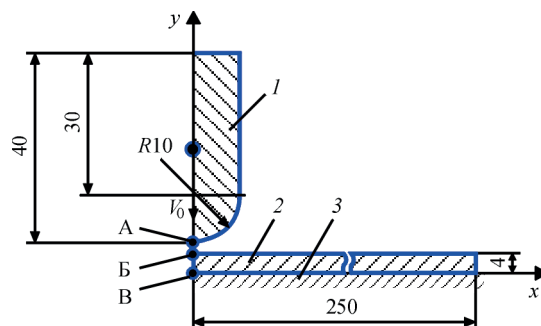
Розрахункова схема процесу динамічного навантаження пластин, що обробляються ЕДО: 1 – електрод-індентор; 2 – зразок, що обробляється; 3 – абсолютно жорстка основа, 4 – точка на зовнішній поверхні електрода-індентора; B – пластини; B – на зворотній поверхні пластини
